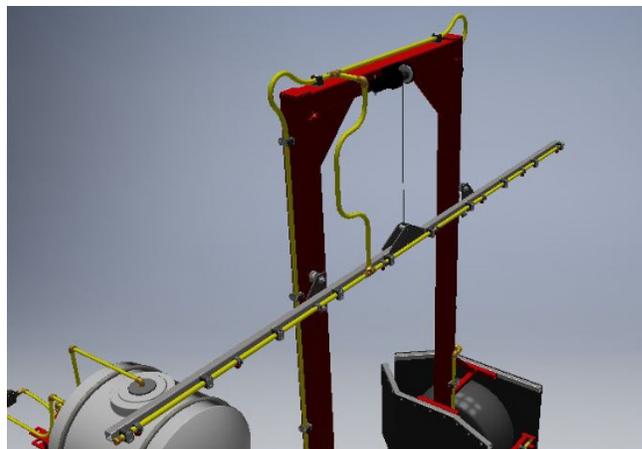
Système de poulie pour ajuster la hauteur de la rampe
